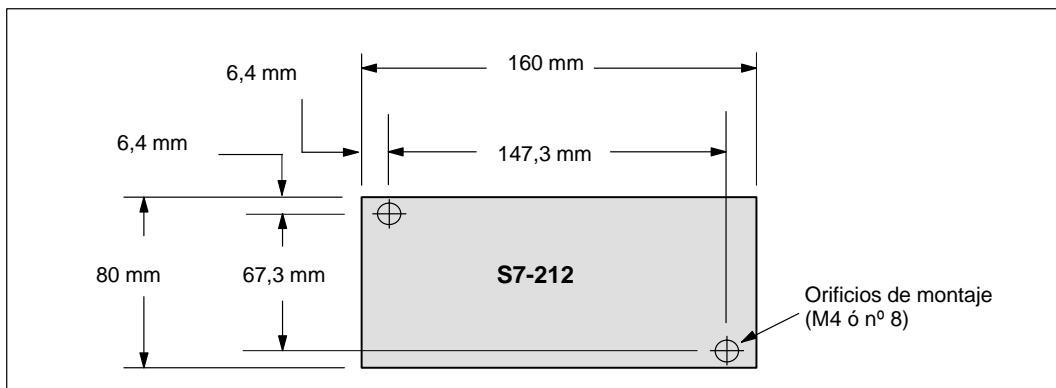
Dimensiones de montaje para una CPU S7-212
